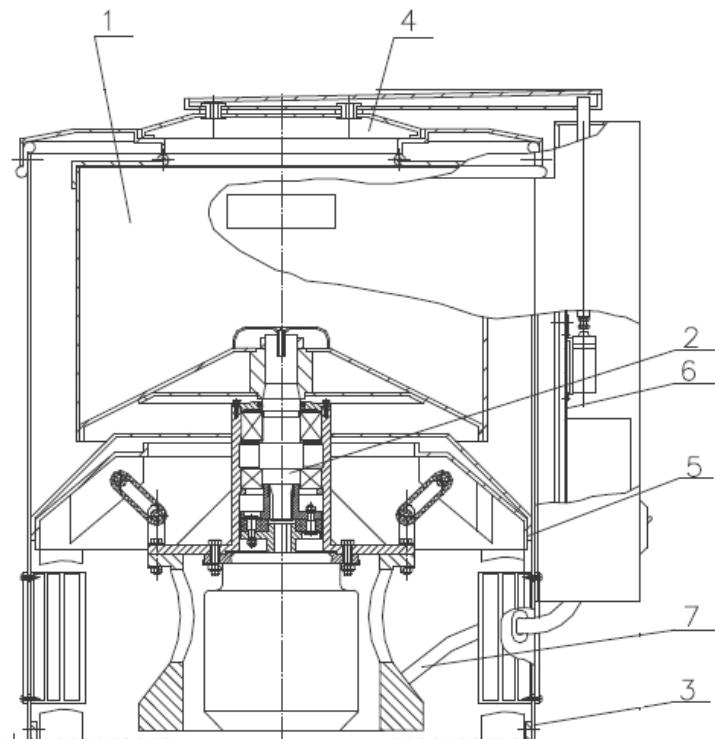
Общий вид центрифуги ЛЦ-25:
